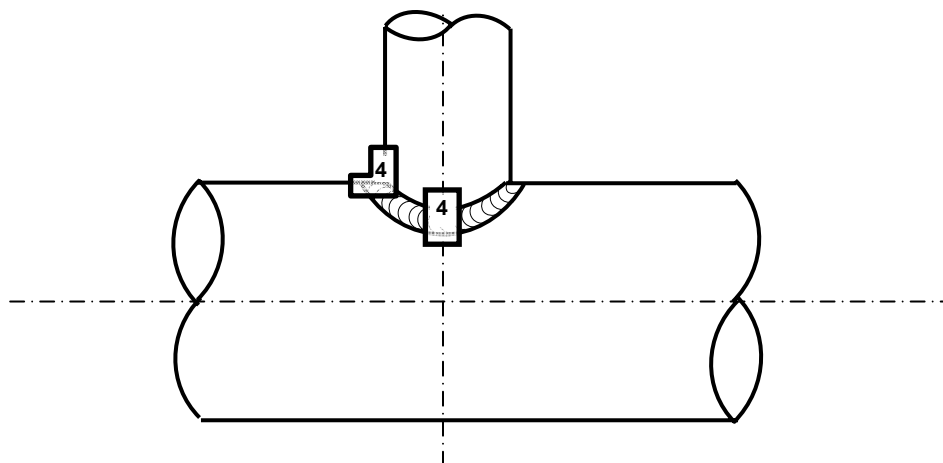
Схема вырезки образцов для проведения механических испытаний при аттестации технологии ремонта методом вырезки отверстий с последующей сваркой (вваркой) патрубков:
